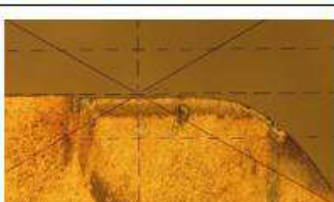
Пластина из быстрорежущей стали Р12МЗК5Ф2-МП с комплексной обработкой (точение жаропрочного сплава; режущий инструмент – Р12МЗК5Ф2-МП с комплексной обработкой)
